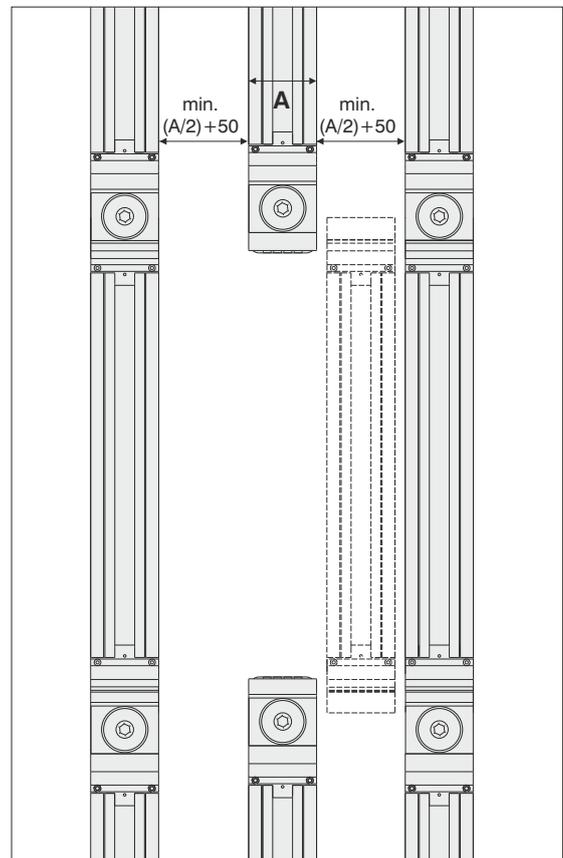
CROISEMENT D'UNE POUTRE EN POSITION HORIZONTALE
